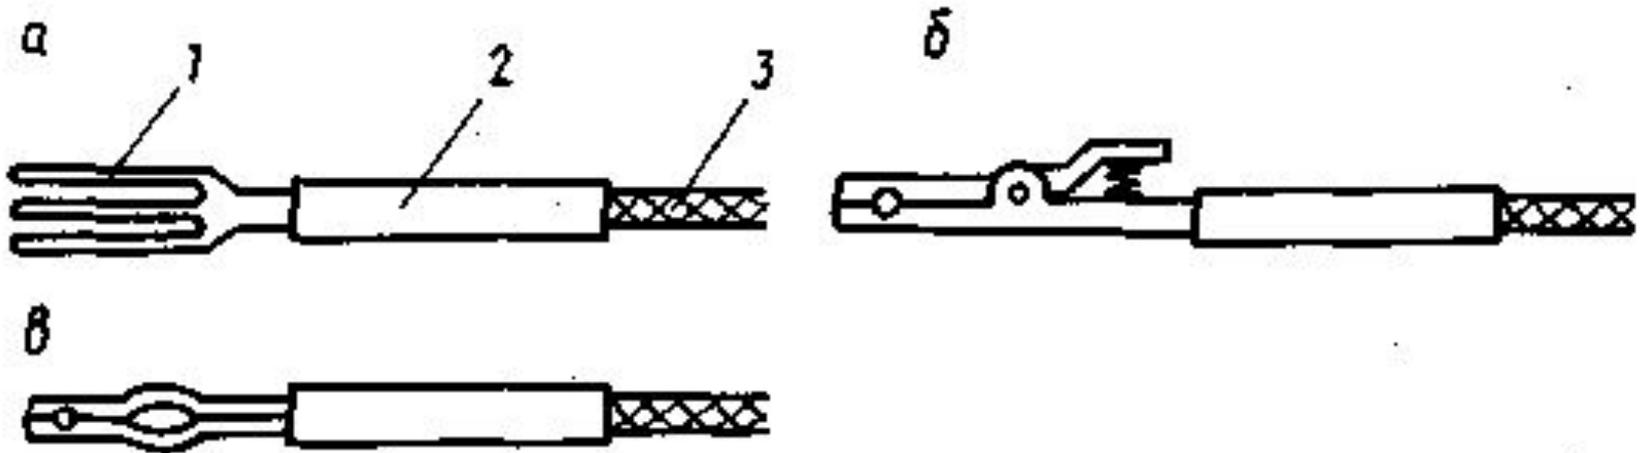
Электрододержатели для ручной дуговой сварки:
